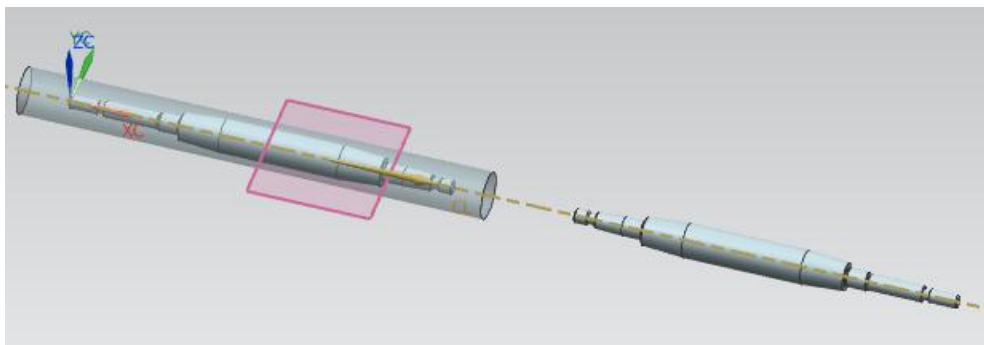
Вид детали с прозрачной заготовкой
